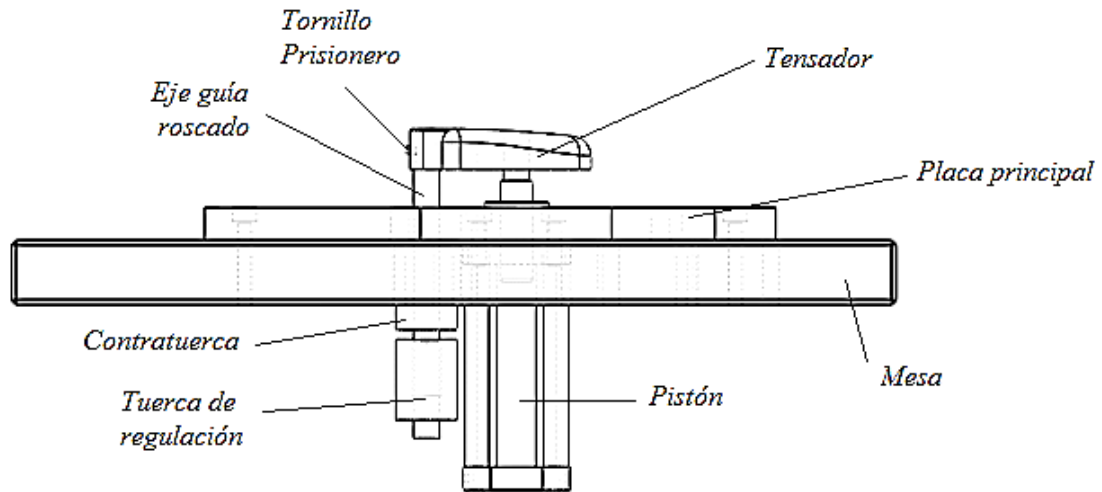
Partes del sistema de salida del vástago del pistón principal
